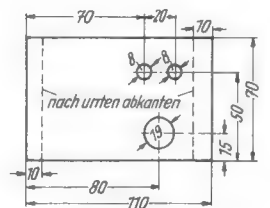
Generator-Chassis, Aluminium 1,5 mm
